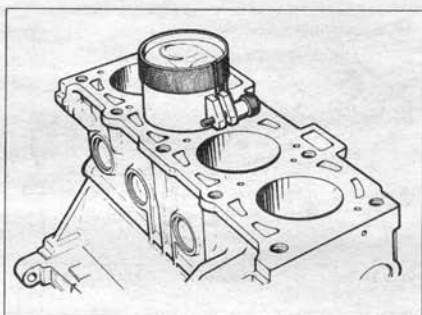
Установка поршня с поршневыми кольцами в цилиндр при помощи регулируемой втулки 67.7854.9519
